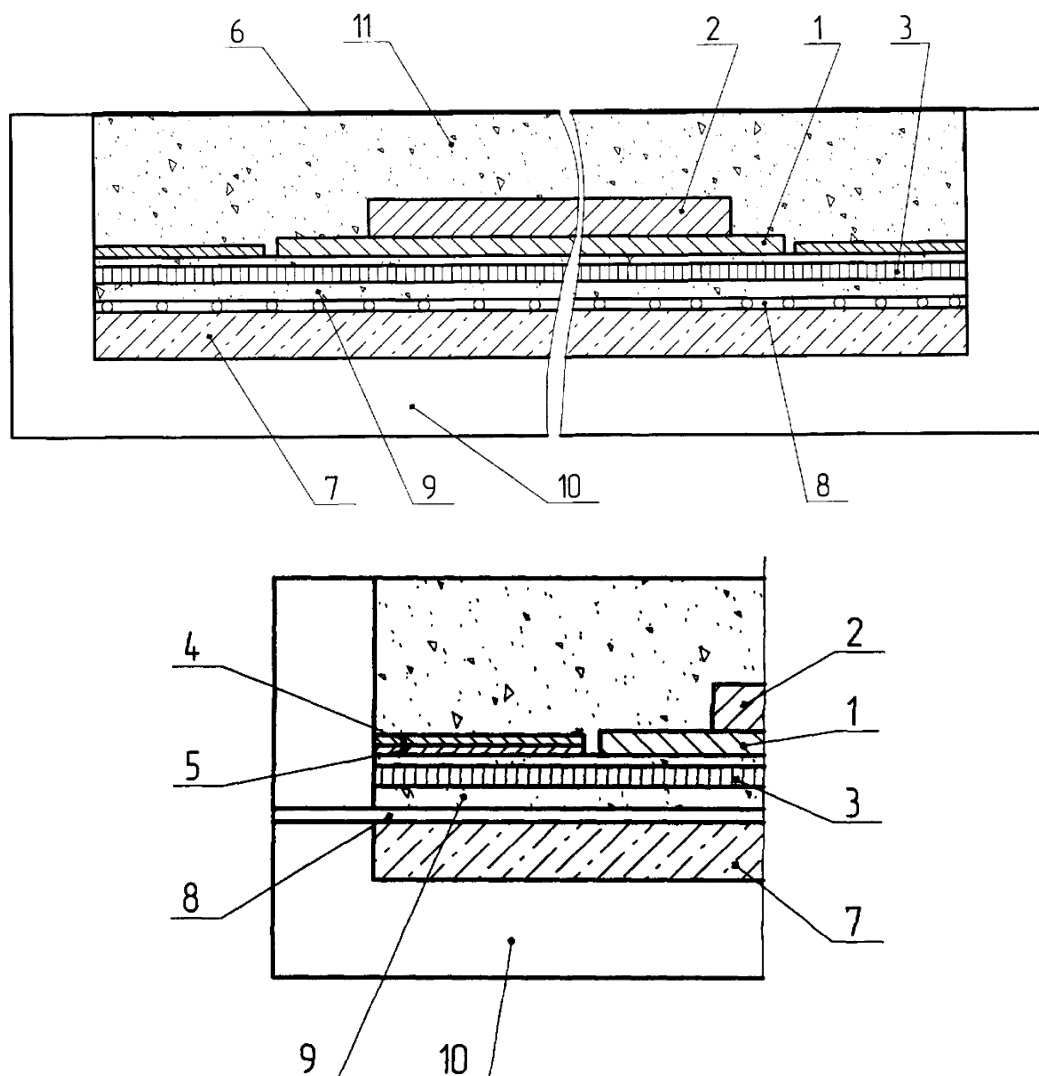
Схема печи для крип-отжига и правки крупногабаритных титановых листов: 1 – металлическая плита; 2 – титановые листы; 3 – основные нагреватели – резисторы; 4 – боковые плиты; 5 – дополнительные нагревательные резисторы; 6 – пленка; 7 – опорные бетонные блоки; 8 – трубы охлаждения; 9 – керамическая плита; 10 – корпус; 11 – сыпучий материал
